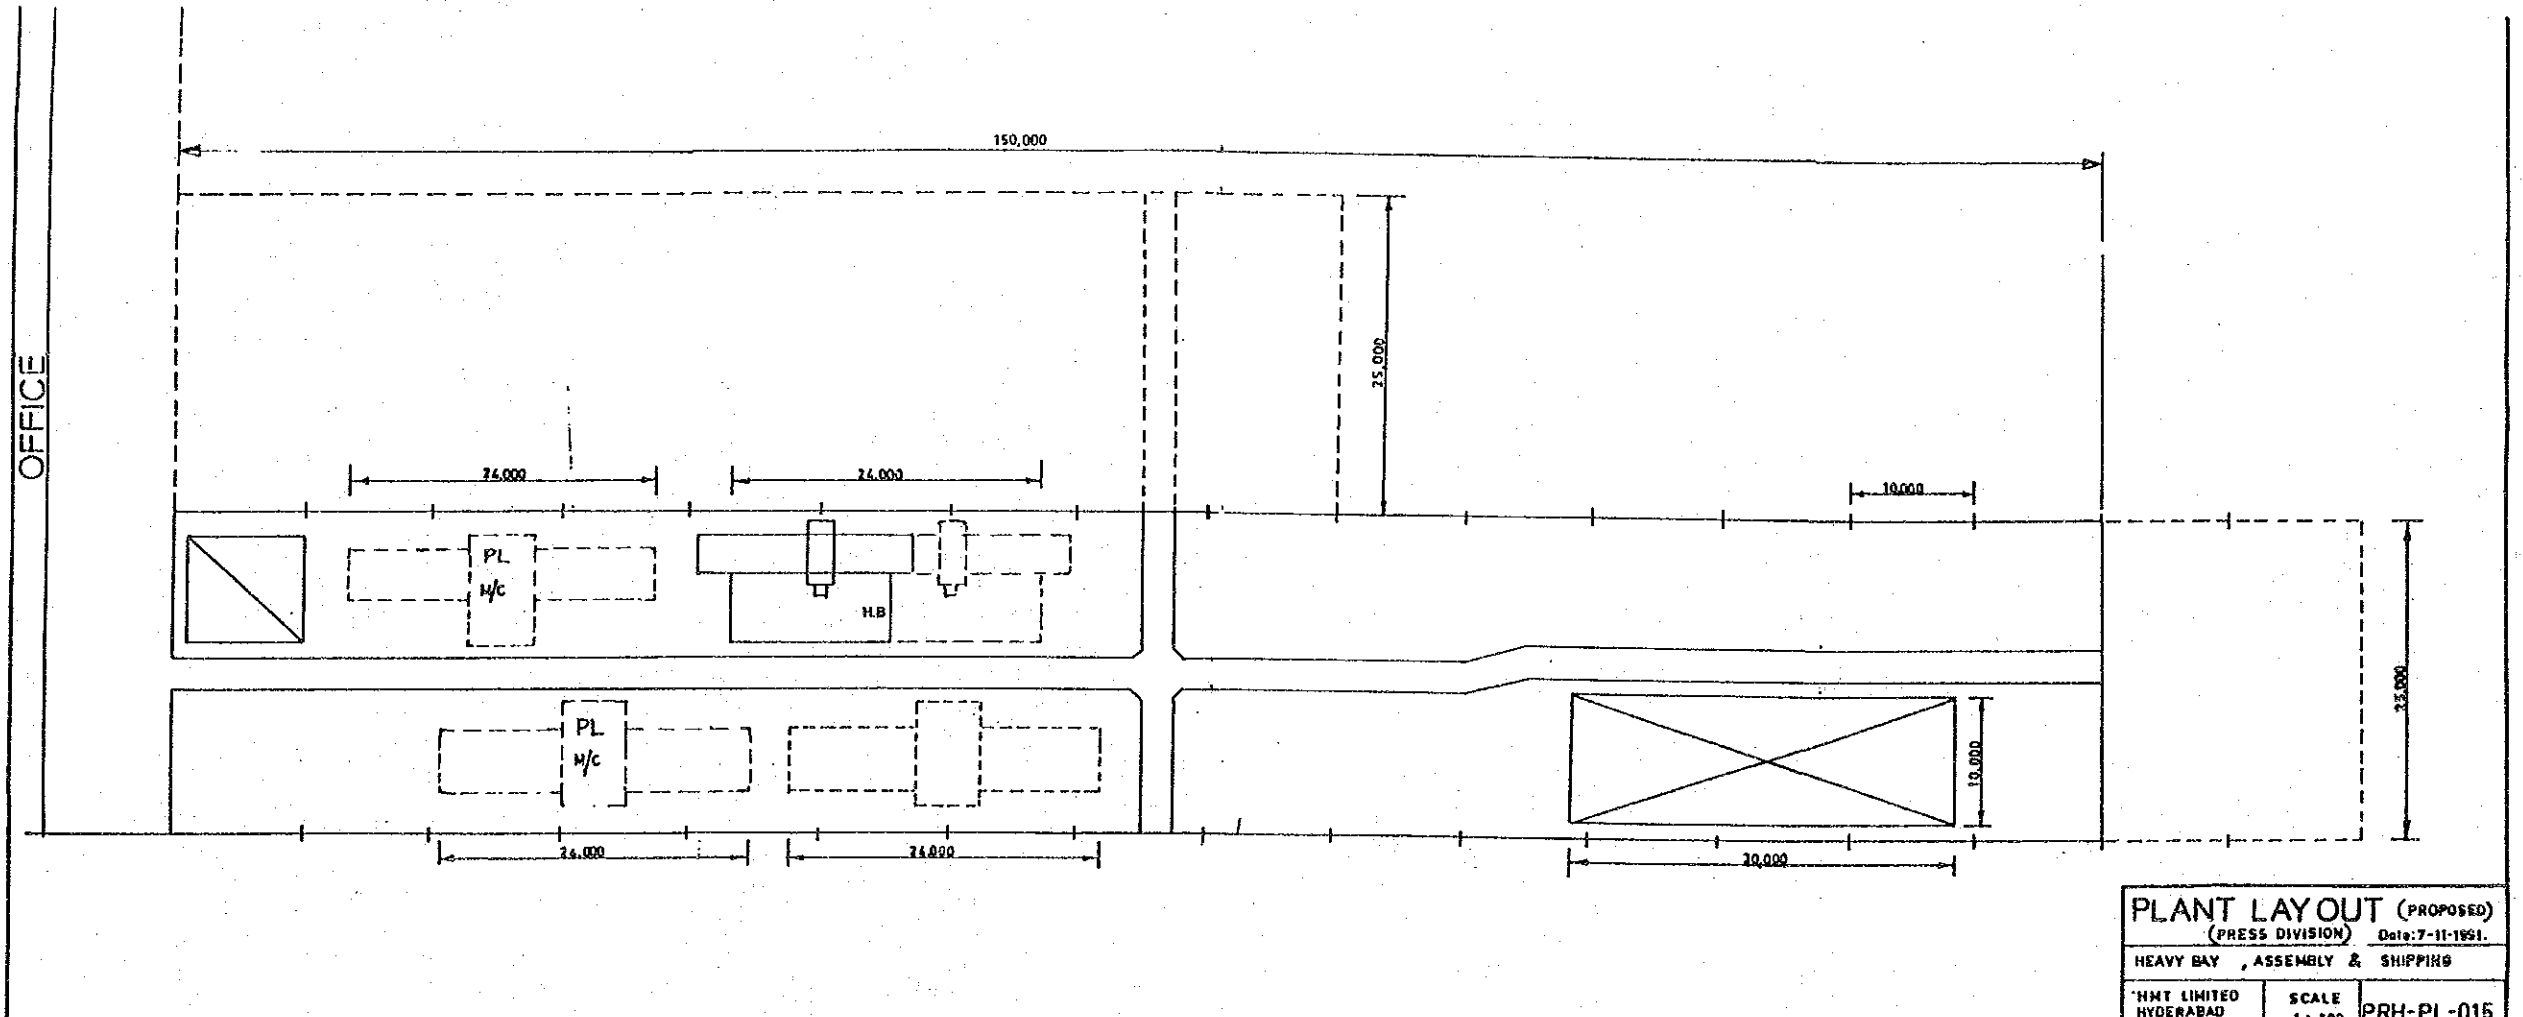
PLANT LAYOUT (PROPOSED)
